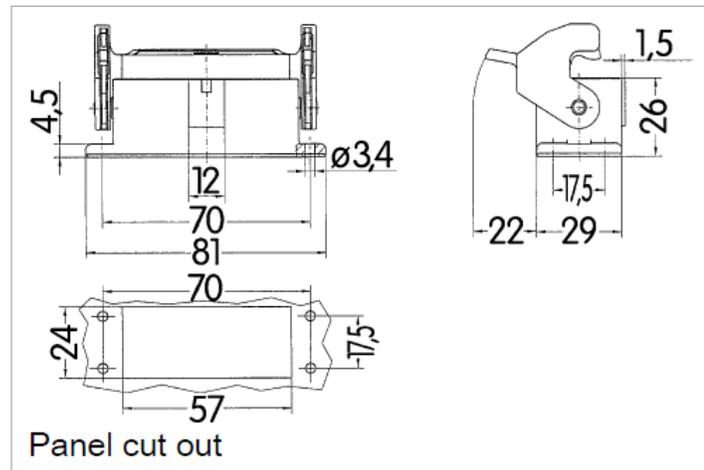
Dimensiones del inserto Harting Han 10 A®
